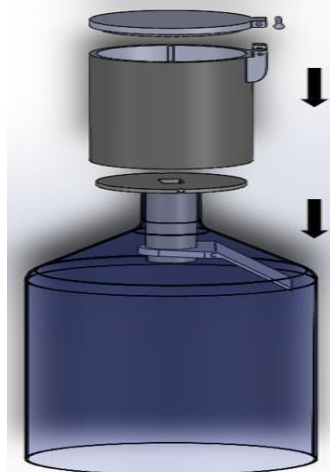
Vista de las piezas ensambladas. Fuente: Elaboración Propia.
